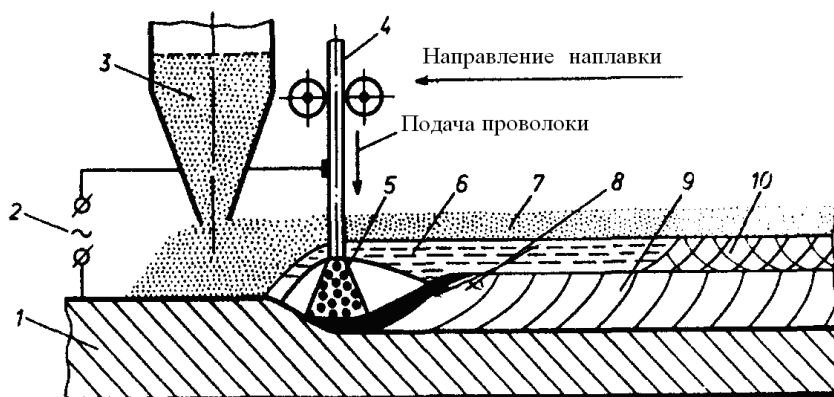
Схема механизированной дуговой наплавки под слоем флюса
